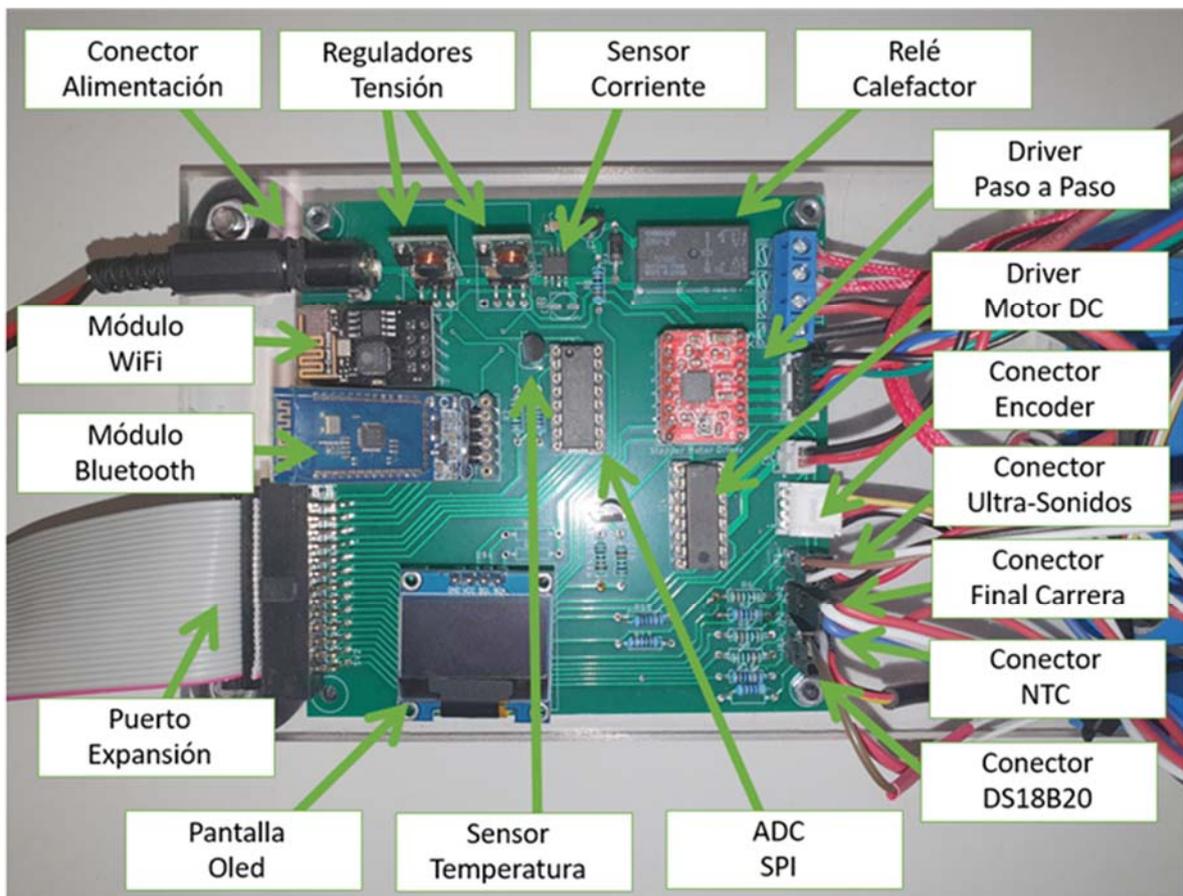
Descripción de la PCB-Control de la Maqueta-XXX-Prog v1
